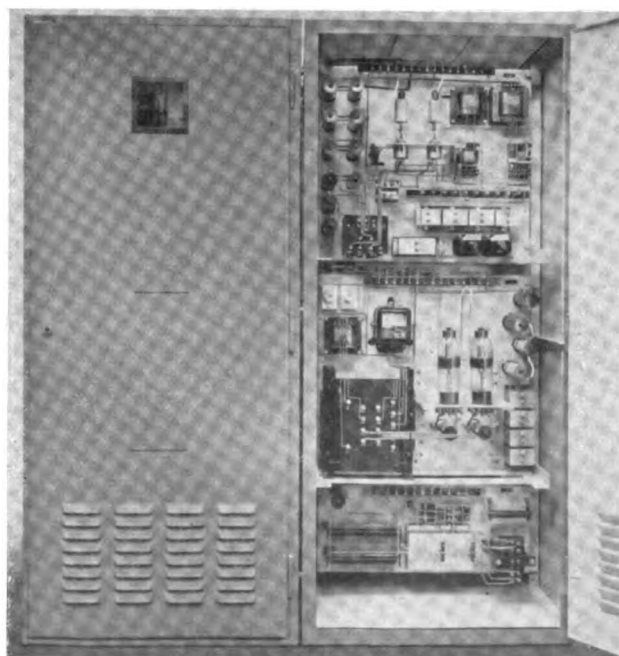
(rechts). Rückansicht eines Schweißtaktters mit den Steuer-tafeln für die Schweißzeit
